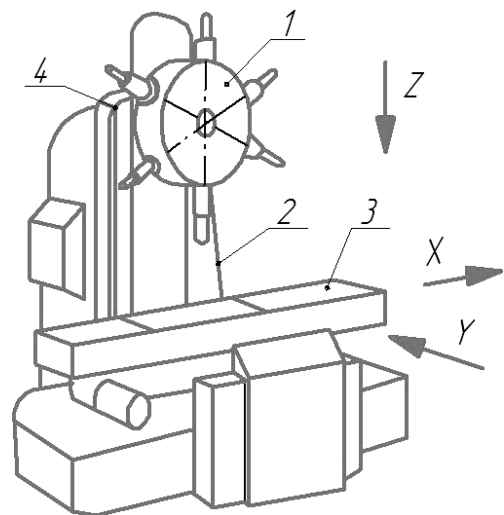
Компоновка вертикально-свердлильного верстата з ЧПК
